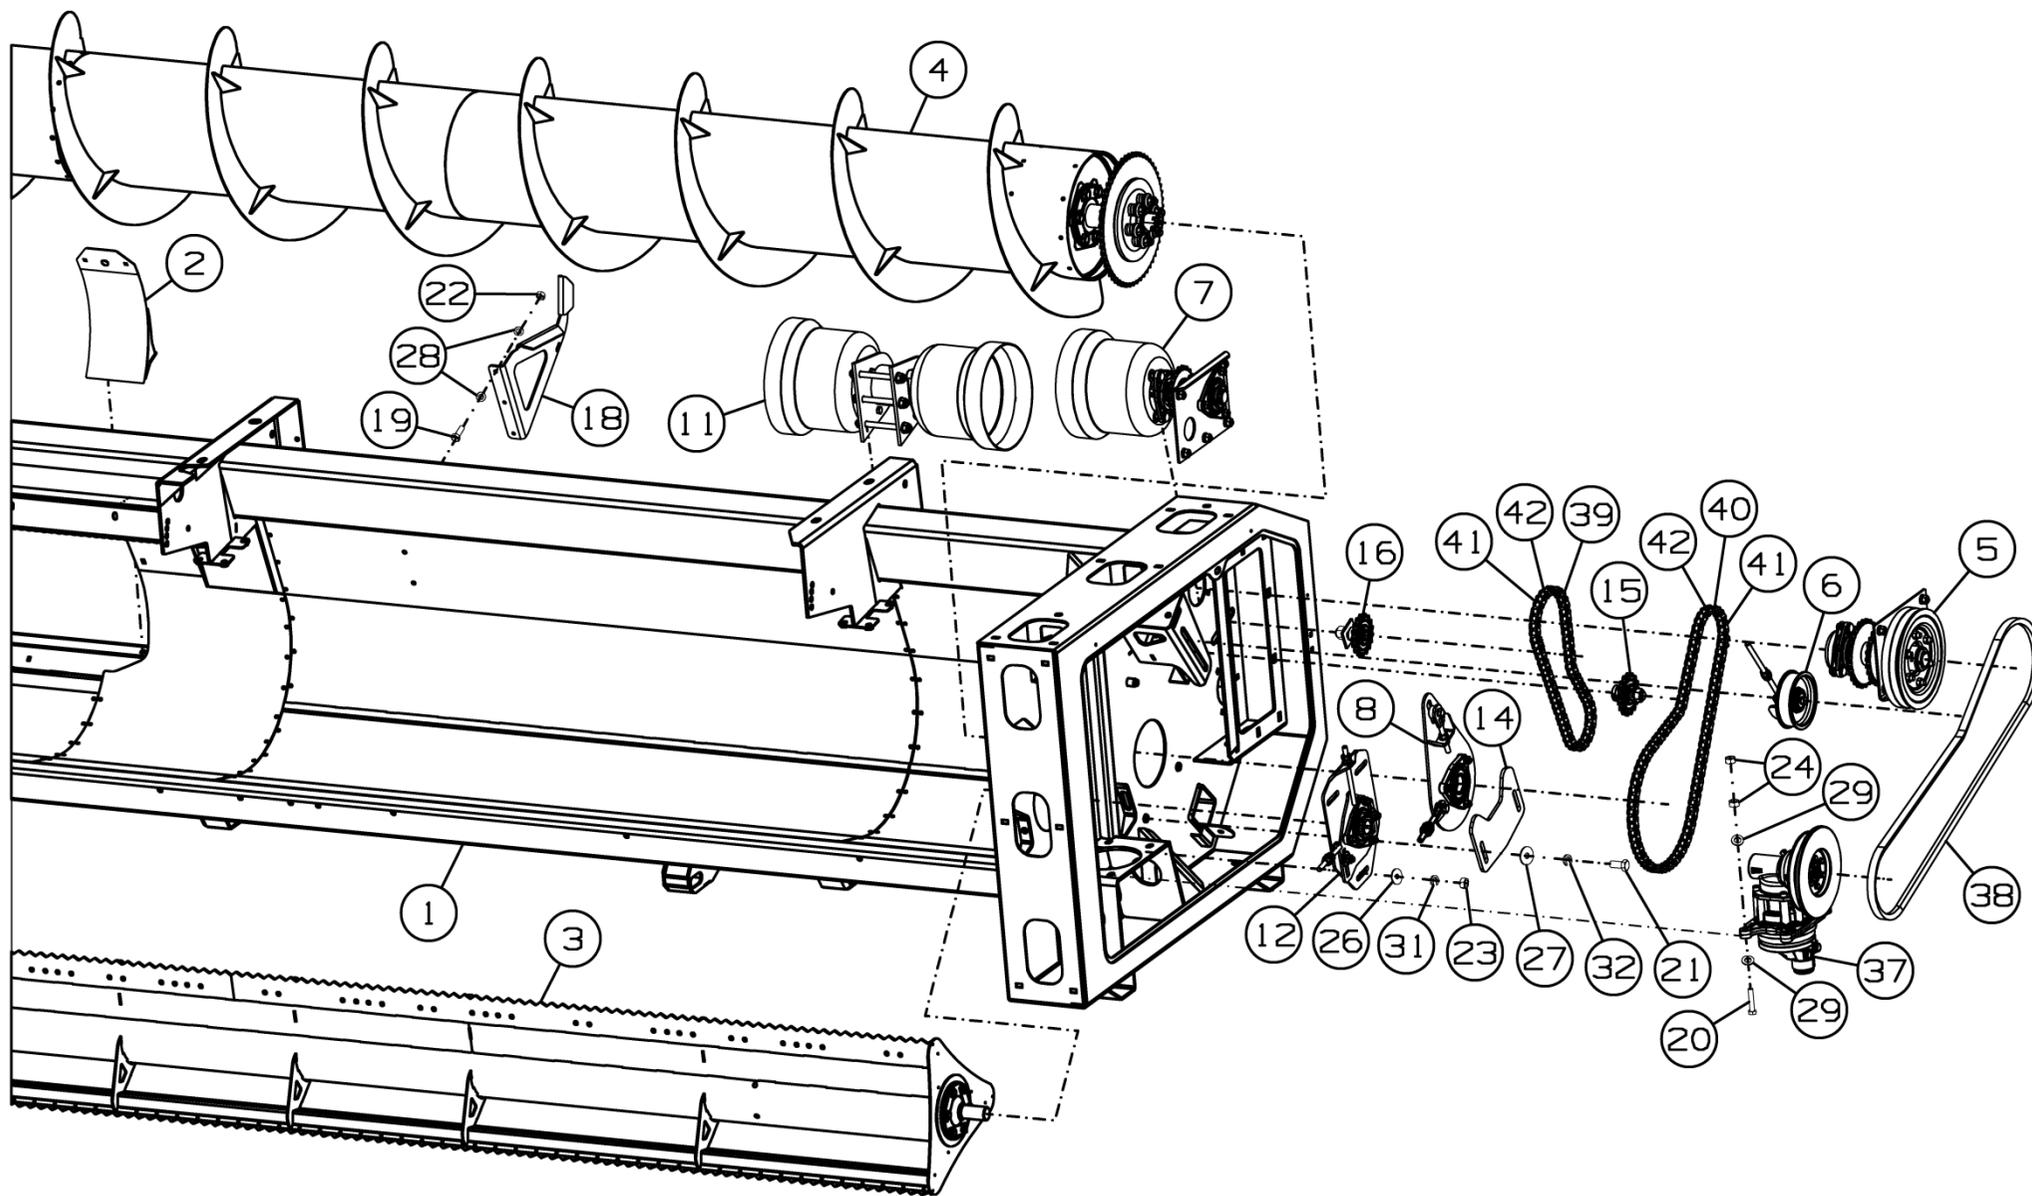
Корпус жатки SS-780.01.01.000У (левая сторона)
